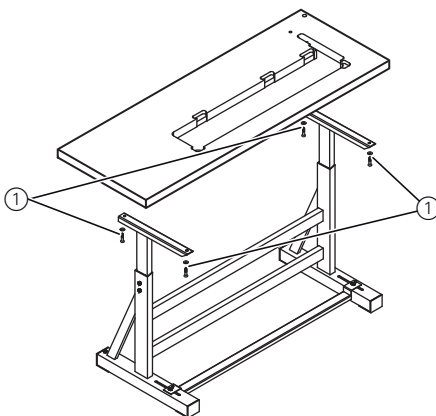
Kompletace desky stolu s dlouhým ramenem
